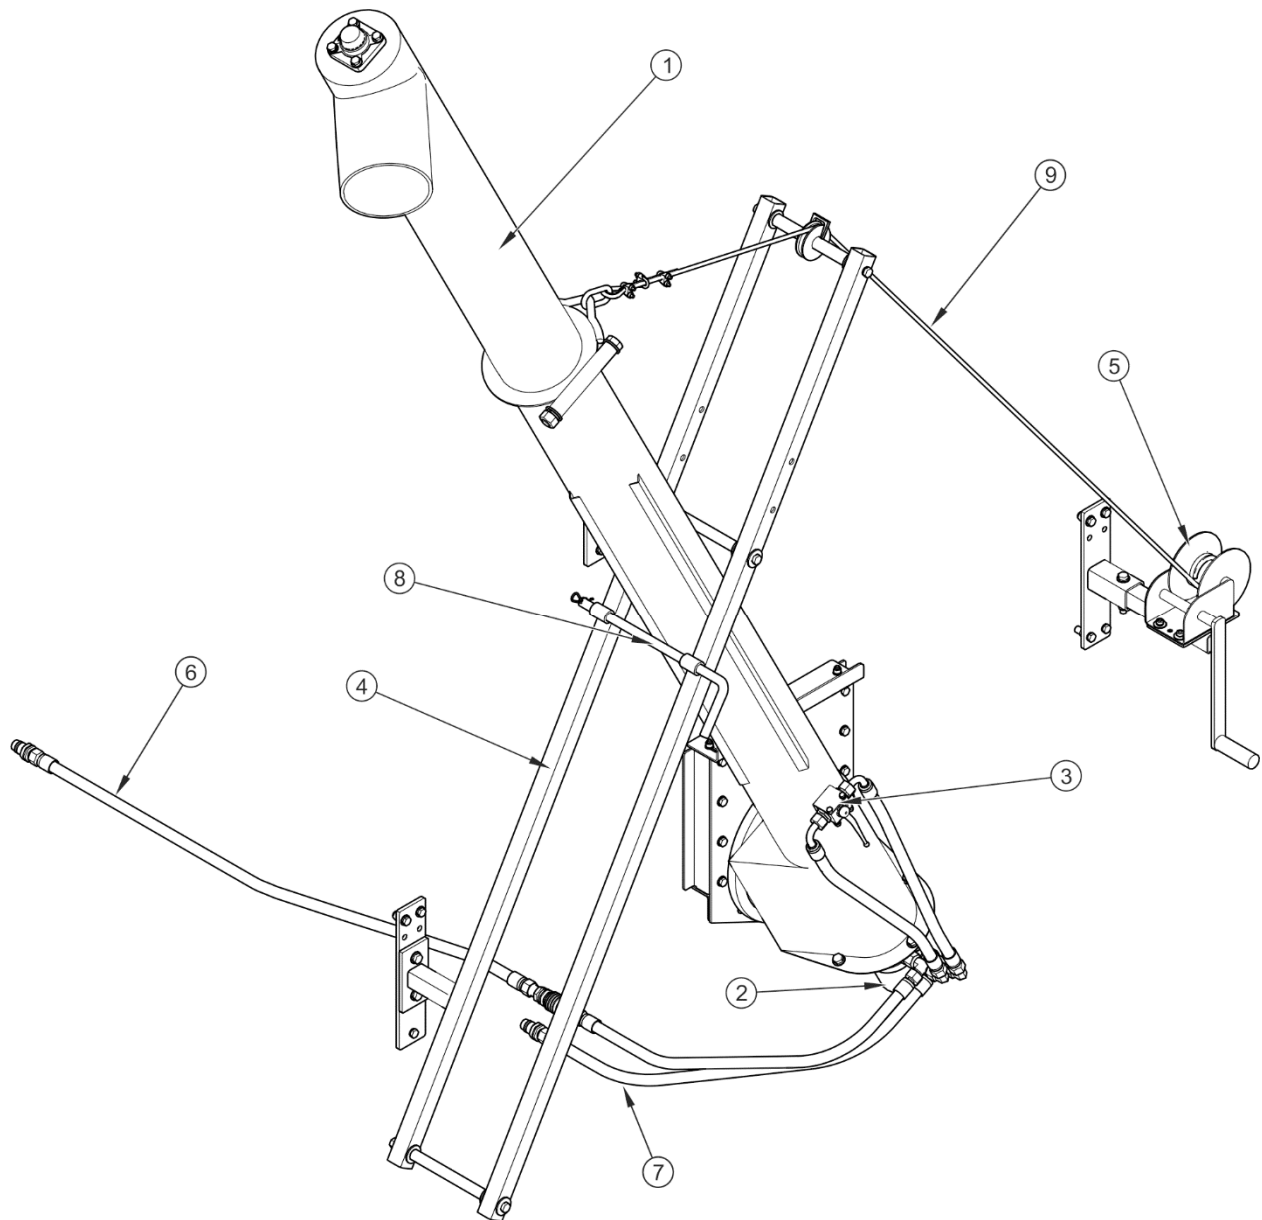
Construction de l'installation hydraulique du distributeur
